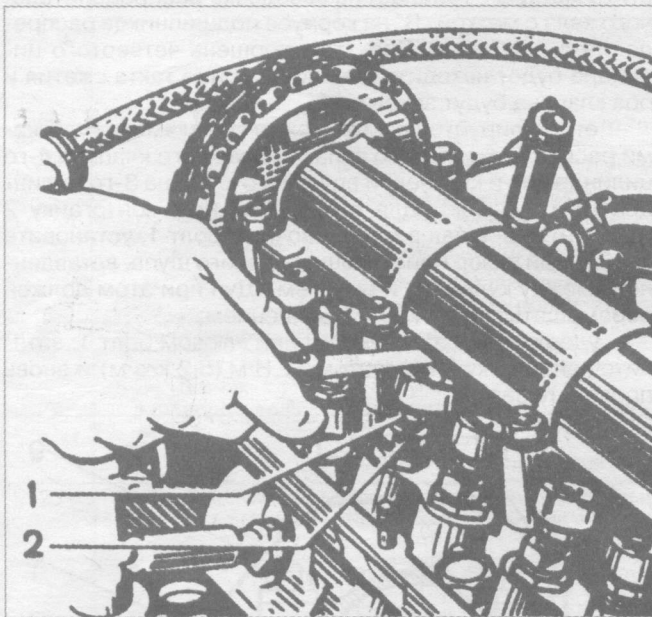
Регулировка зазоров в механизме привода клапанов:
